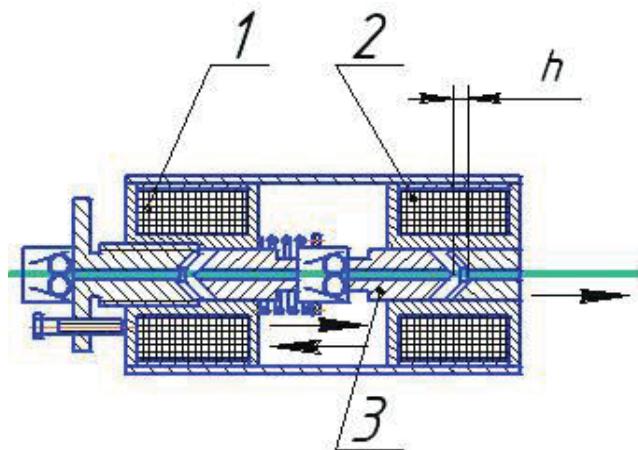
Электромагнитный механизм импульсной подачи сварочной проволоки с двумя электромагнитами: 1,2 – катушки; 3 – якорь; h – зазор
